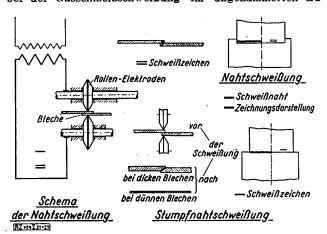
bis 27 Elektrische Nahtschweißung
